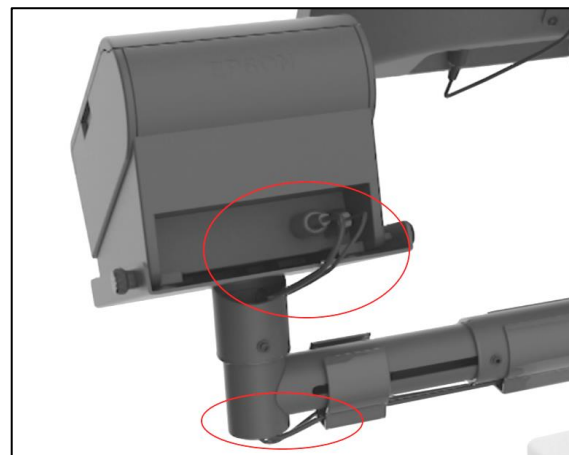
Druckerhalterung; Kabelführung Innen.
